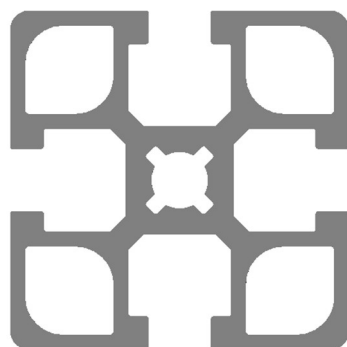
Secção do perfil técnico Minitec 45 x 45 F.
